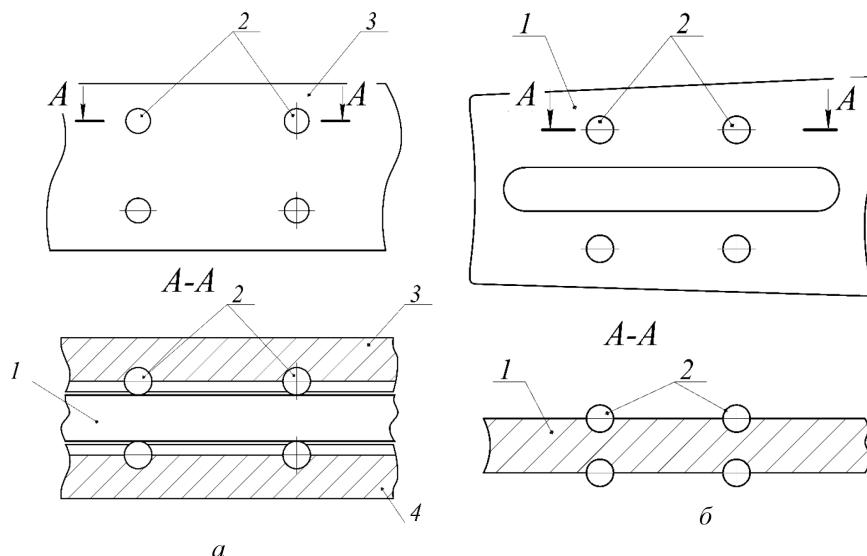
Конструкции подвижной пильной шины с вставленными направляющими шариками: *a* – в корпусе и крышке; *б* – в пильной шине (*1* – шина; *2* – направляющие шарики; *3* – корпус; *4* – крышка)
